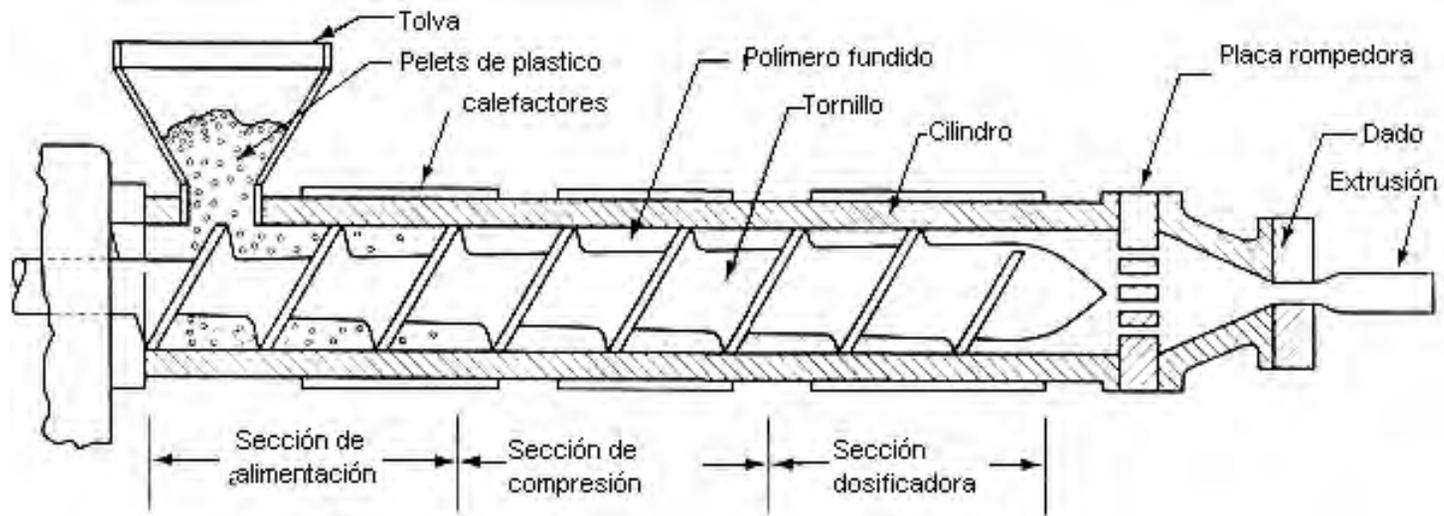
Diseño de la máquina utilizada para la técnica de extrusión. (51)
